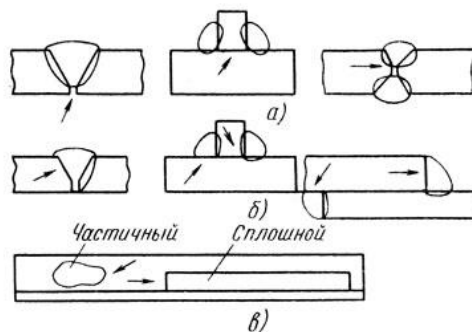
Непровары: а - корня шва, б - зоны сплавления, в - частичный и сплошной
